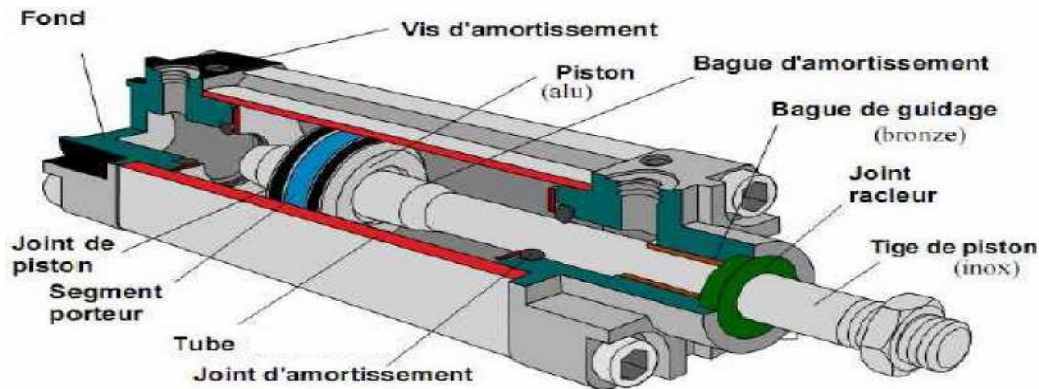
Vue en coupe d'un vérin pneumatique.
